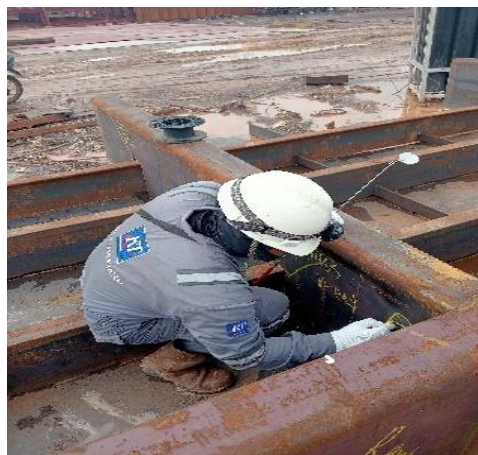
10 *Inspect welding panel main deck.
